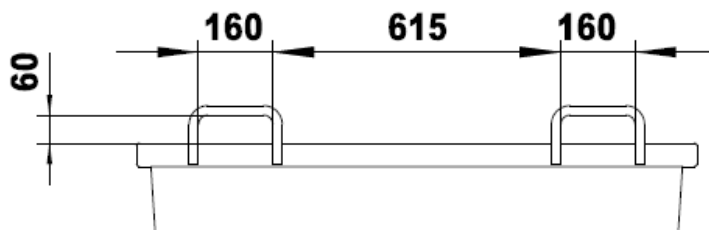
Dimensioner bøjle på universal-beholder type UC
